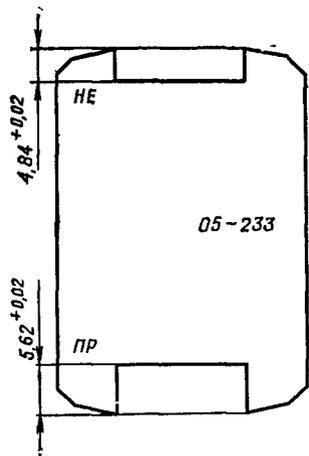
Шаблон для проверки выступающего переднего стопора 8У35 05-233
